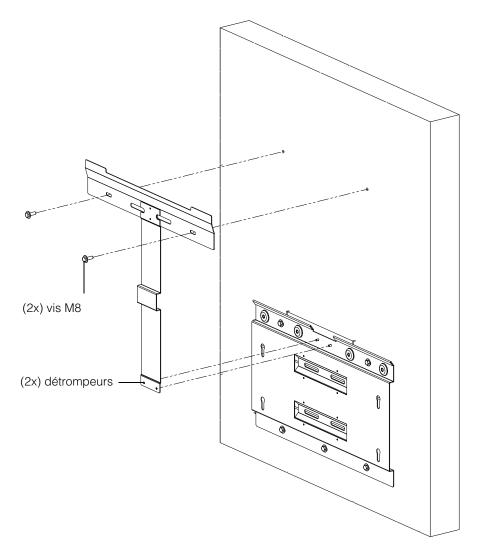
Fixation du support de montage de l'onduleur au mur
